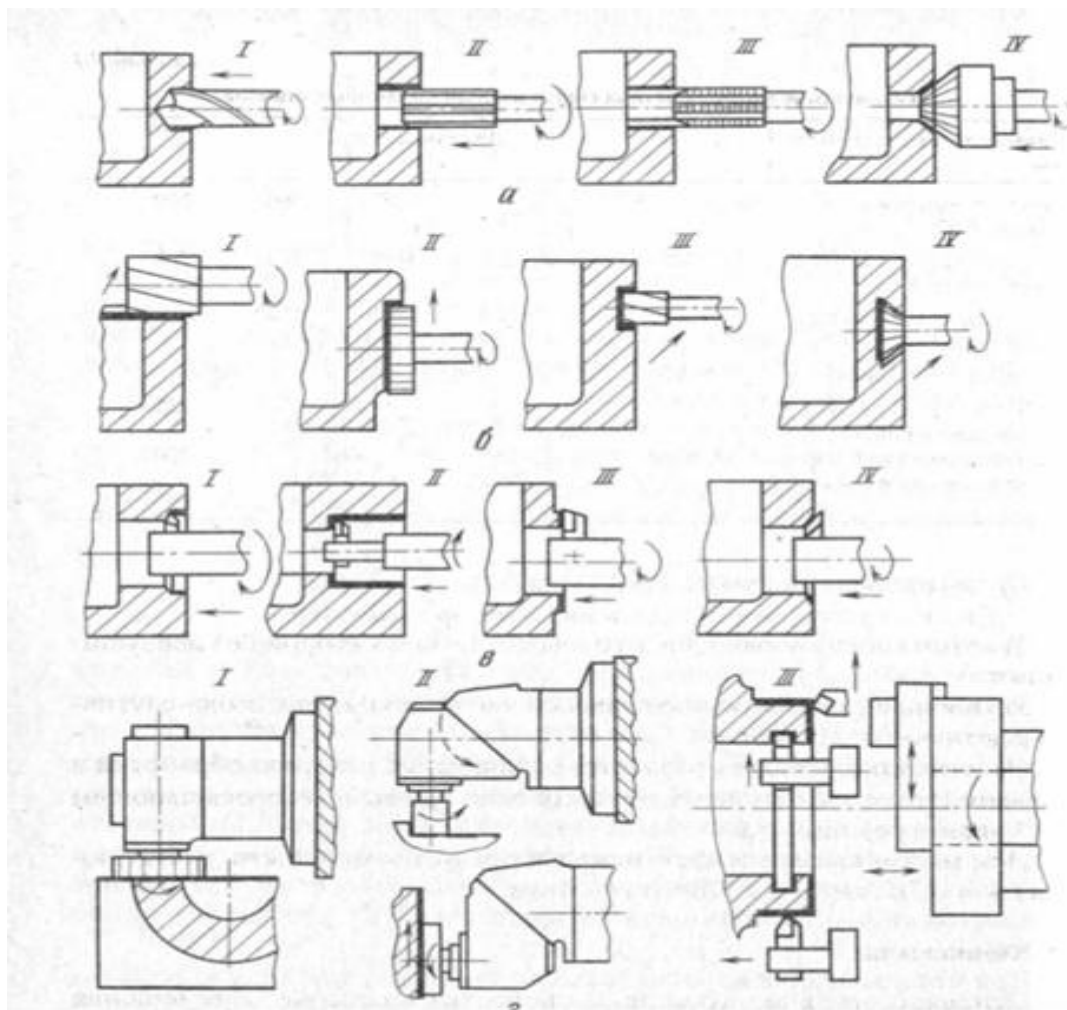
Схемы обработки различных поверхностей на горизонтально-расточном станке: сверление, развертывание, нарезание резьбы метчиком (схемы а I, II, III, IV), фрезерование (схема б, I) цилиндрической, торцевой (схема б, II), концевой (схема б, III), угловой (схема б, IV) фрезами, растачивание: сквозных отверстий (схема в, I), с подрезкой торца (схема в, II), подрезка торца (схема в, III), получение конической поверхности (схема в, IV); обработка различных поверхностей с использованием дополнительных приспособлений: горизонтальных плоскостей с помощью угловой фрезерной головки (схема г, I); взаимно перпендикулярных плоскостей с помощью поворотной на 90° фрезерной головки (схема г, II); наружной поверхности, торца и кольцевой канавки с помощью планшайбы с радиально перемещаемой ползушкой (схема г, III).
